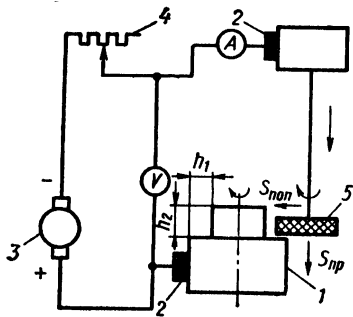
Схема установки для електроконтактної обробки тіл обертання
